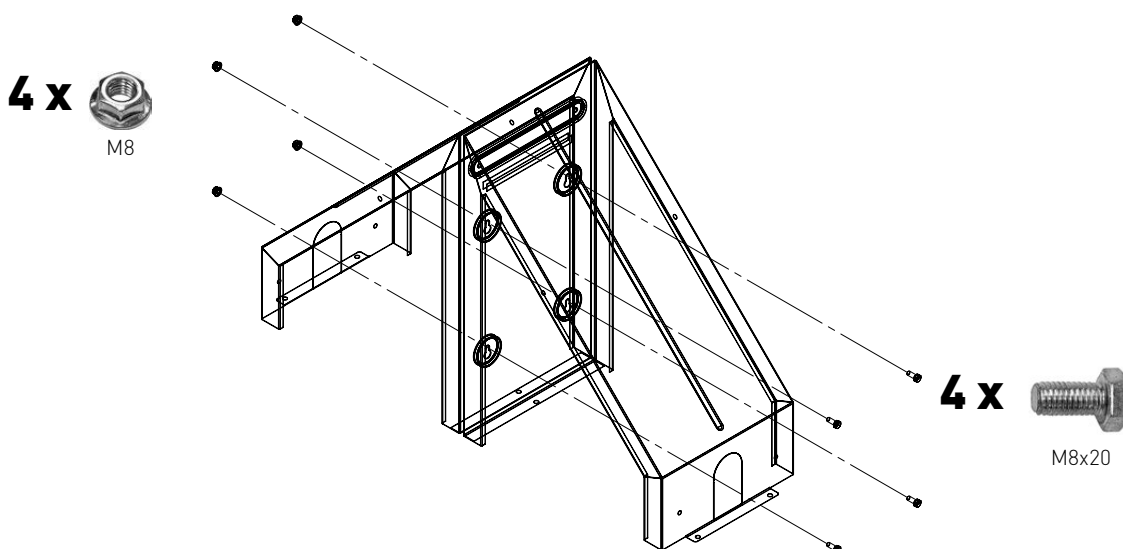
Visser ensemble 2 montants pour former un tunnel
